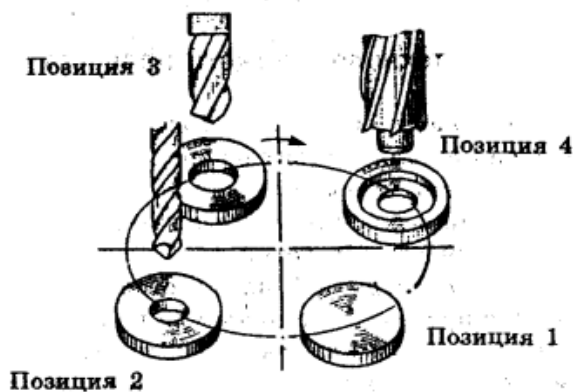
Обработка детали на сверлильном станке: позиция 1 – установка заготовки; позиция 2 – сверление; позиция 3 – зенкерование; позиция 4 – развёртывание
